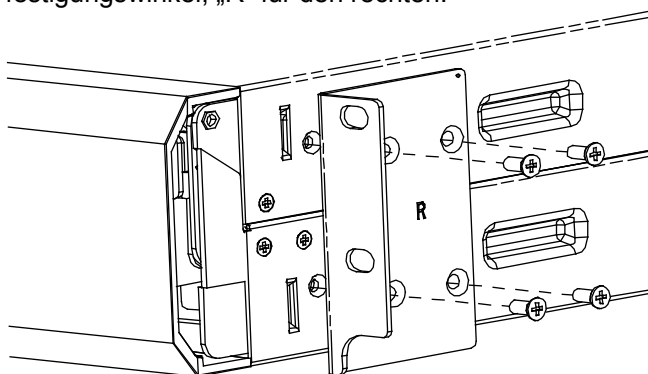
Befestigung des Montagewinkels (hier rechts)
